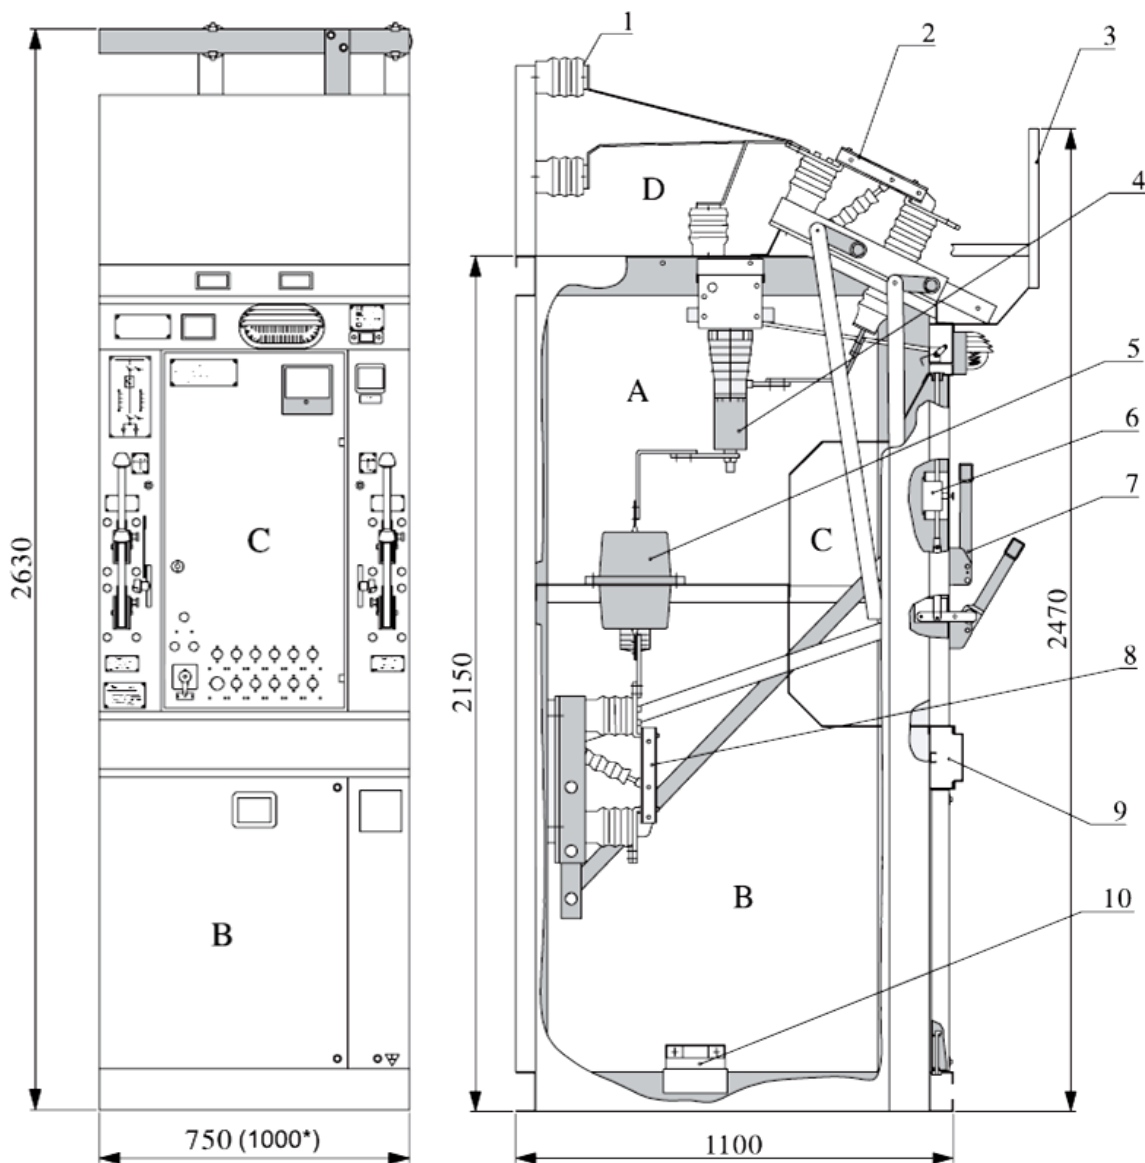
Общий вид камеры КСО – 298 НН:
